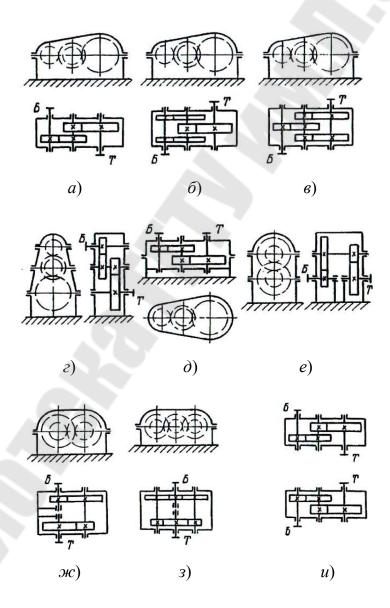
Типовые кинематические схемы цилиндрических редукторов
